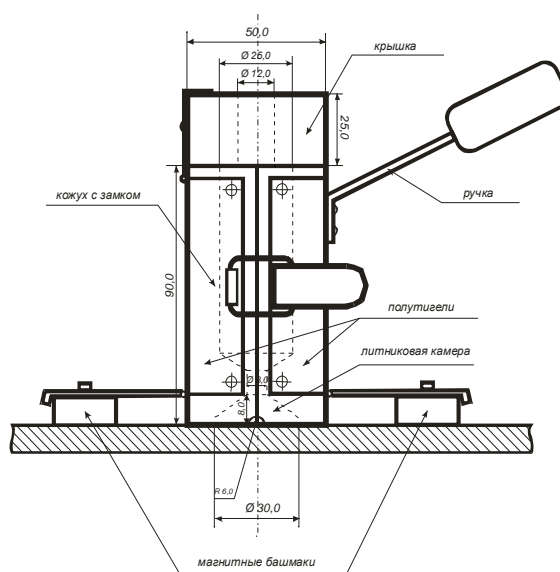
Конструктивные размеры МТФ для приварки выводов ЭХЗ
